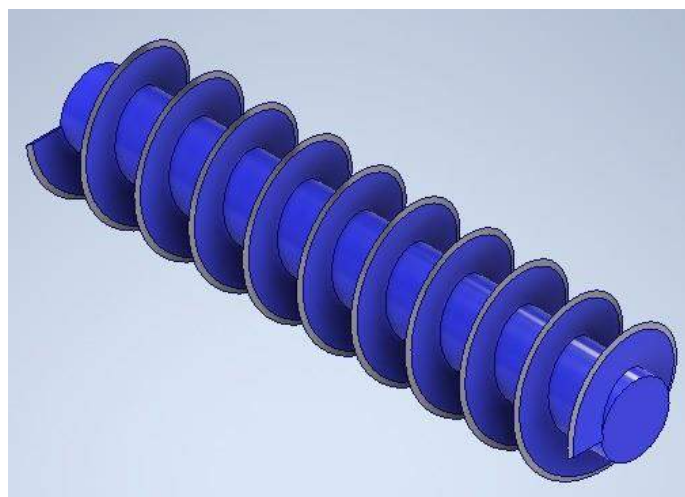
Diseño de forma de la cuchilla en astilladora de tambor.
